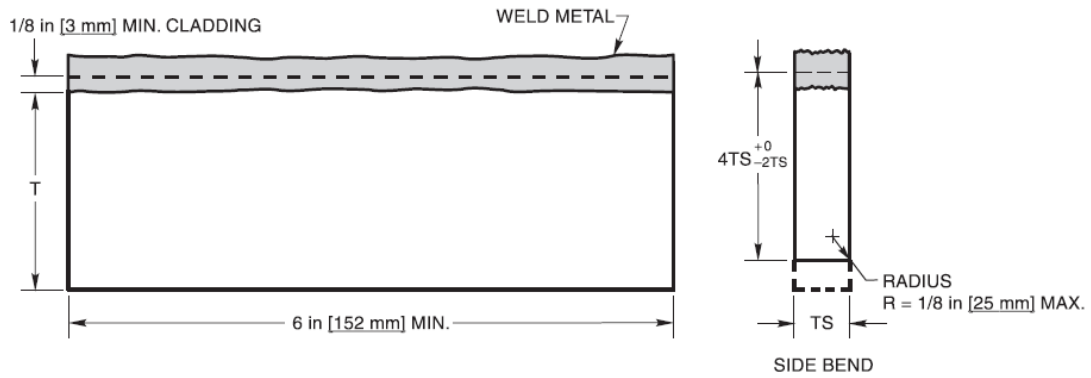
Dimensiones de las probetas para el ensayo de doblado (American Welding Society, 2009).
